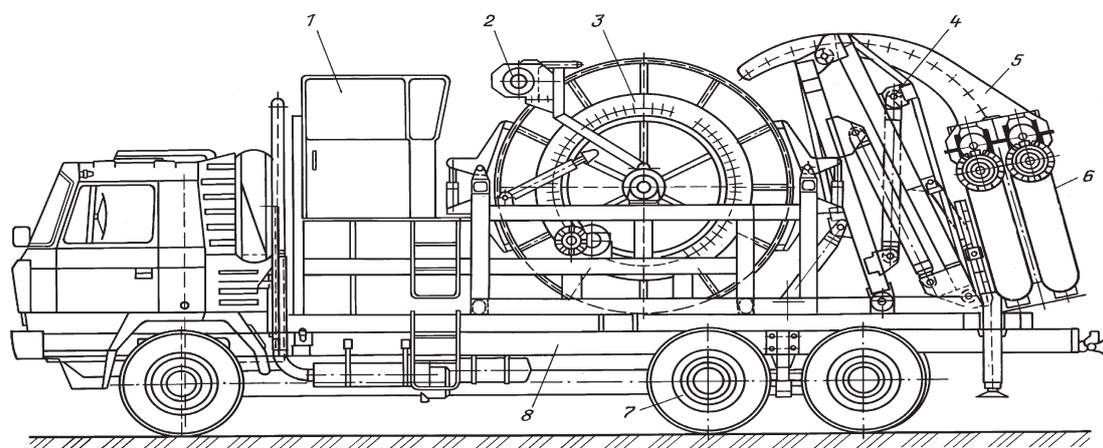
Агрегат АПРС: 1 — кабина оператора; 2 — укладчик гибкой трубы; 3 — барабан с КГТ; 4 — механизм установки транспортера в рабочее положение; 5 — направляющая дуга; 6 — транспортер; 7 — автомобильное шасси; 8 — рама агрегата
